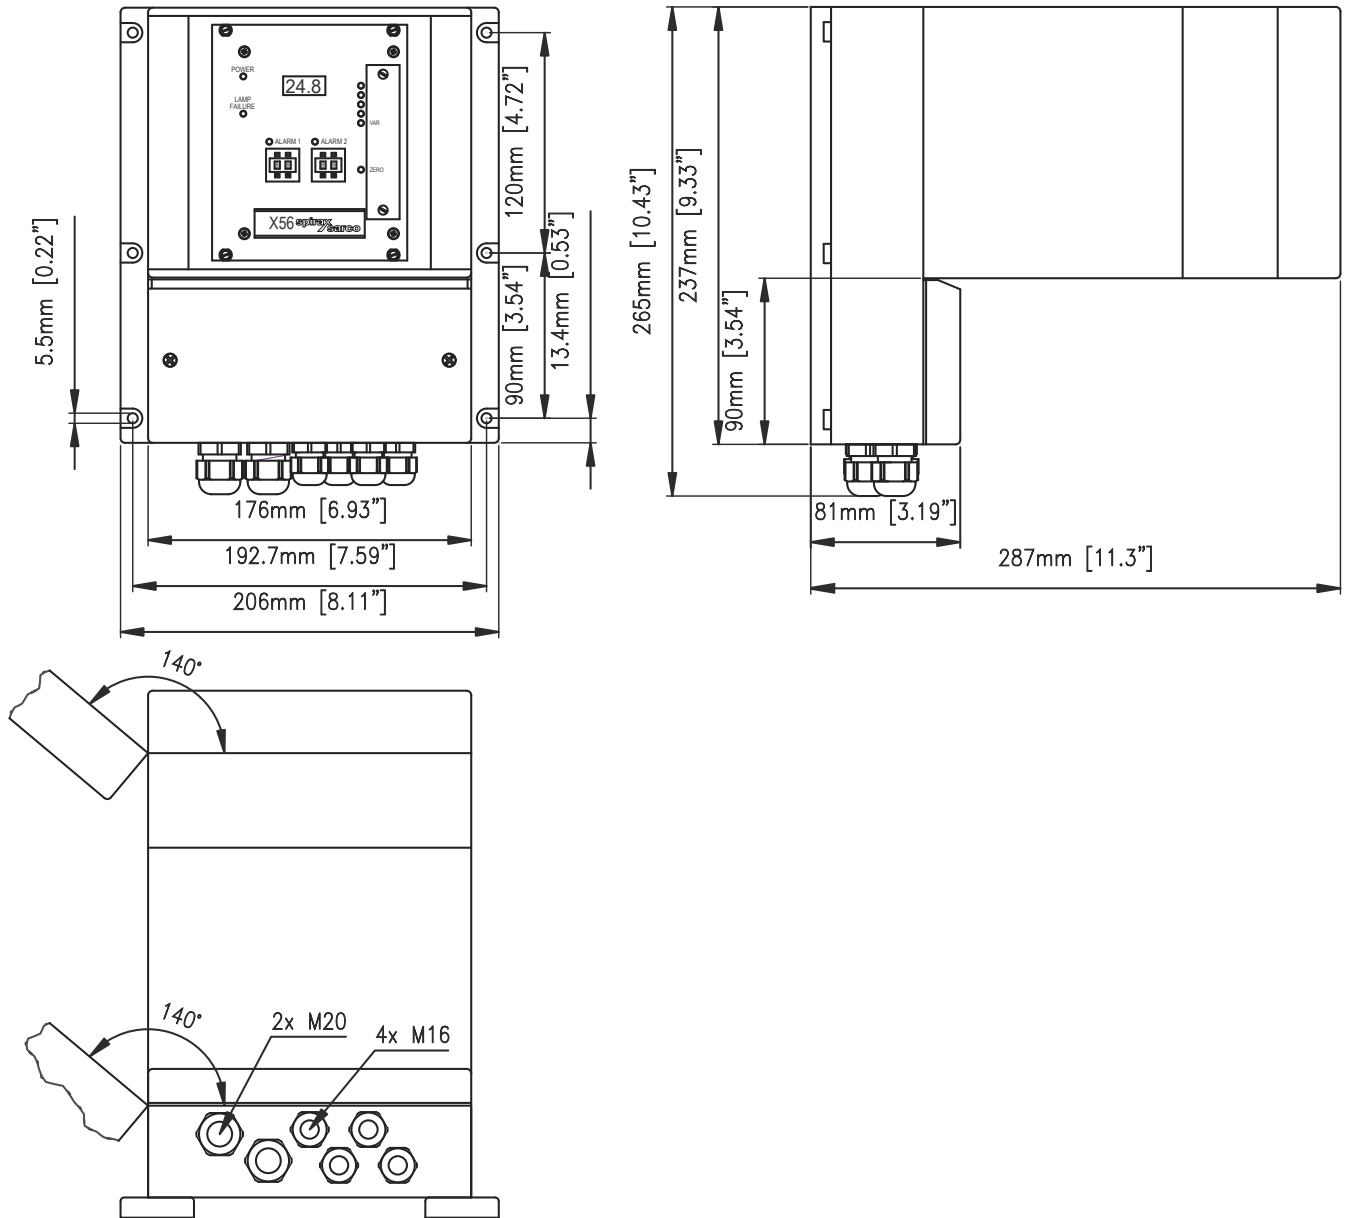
Dimensions avec boîtier B19-21 pour montage mural
